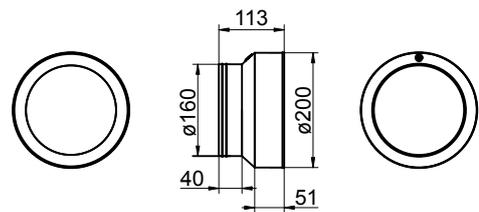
Dimensions de raccord de transition DN160 (dimensions en mm)
